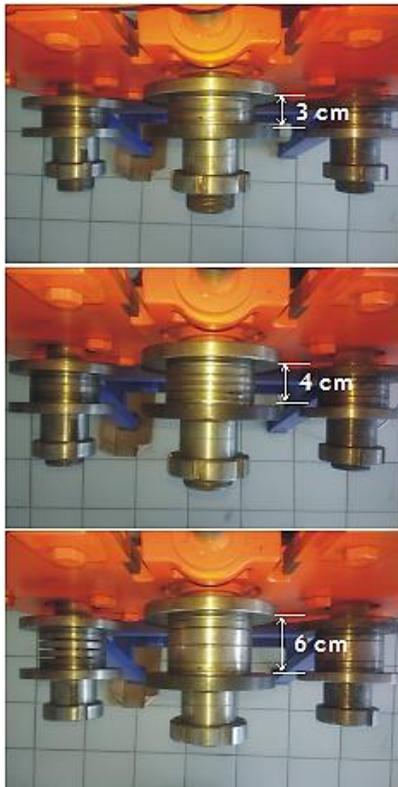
Mesin *Roll Bending* Pipa Persegi
